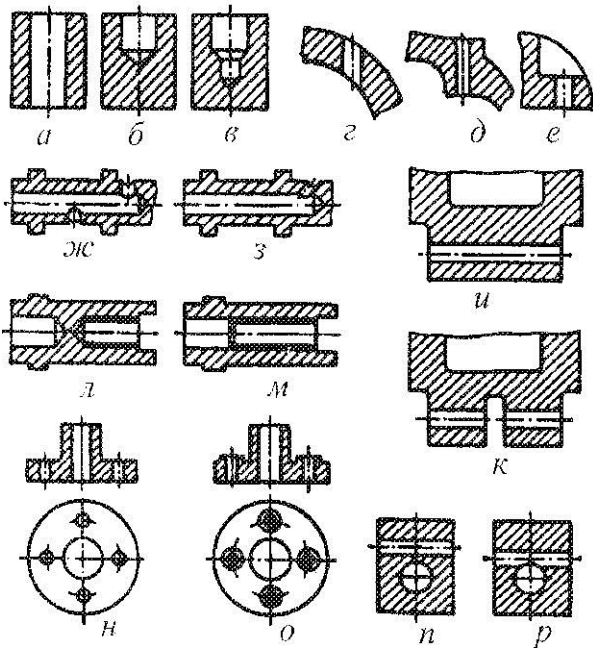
Приклади конструкцій деталей машин, оброблених на свердильних верстатах
